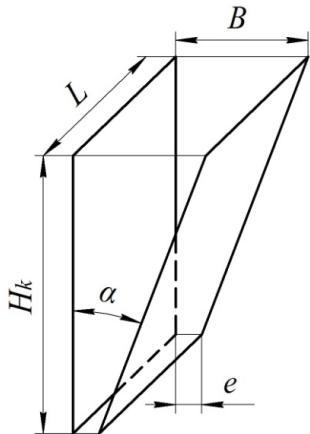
Основные параметры камеры дробления щековой дробилки
